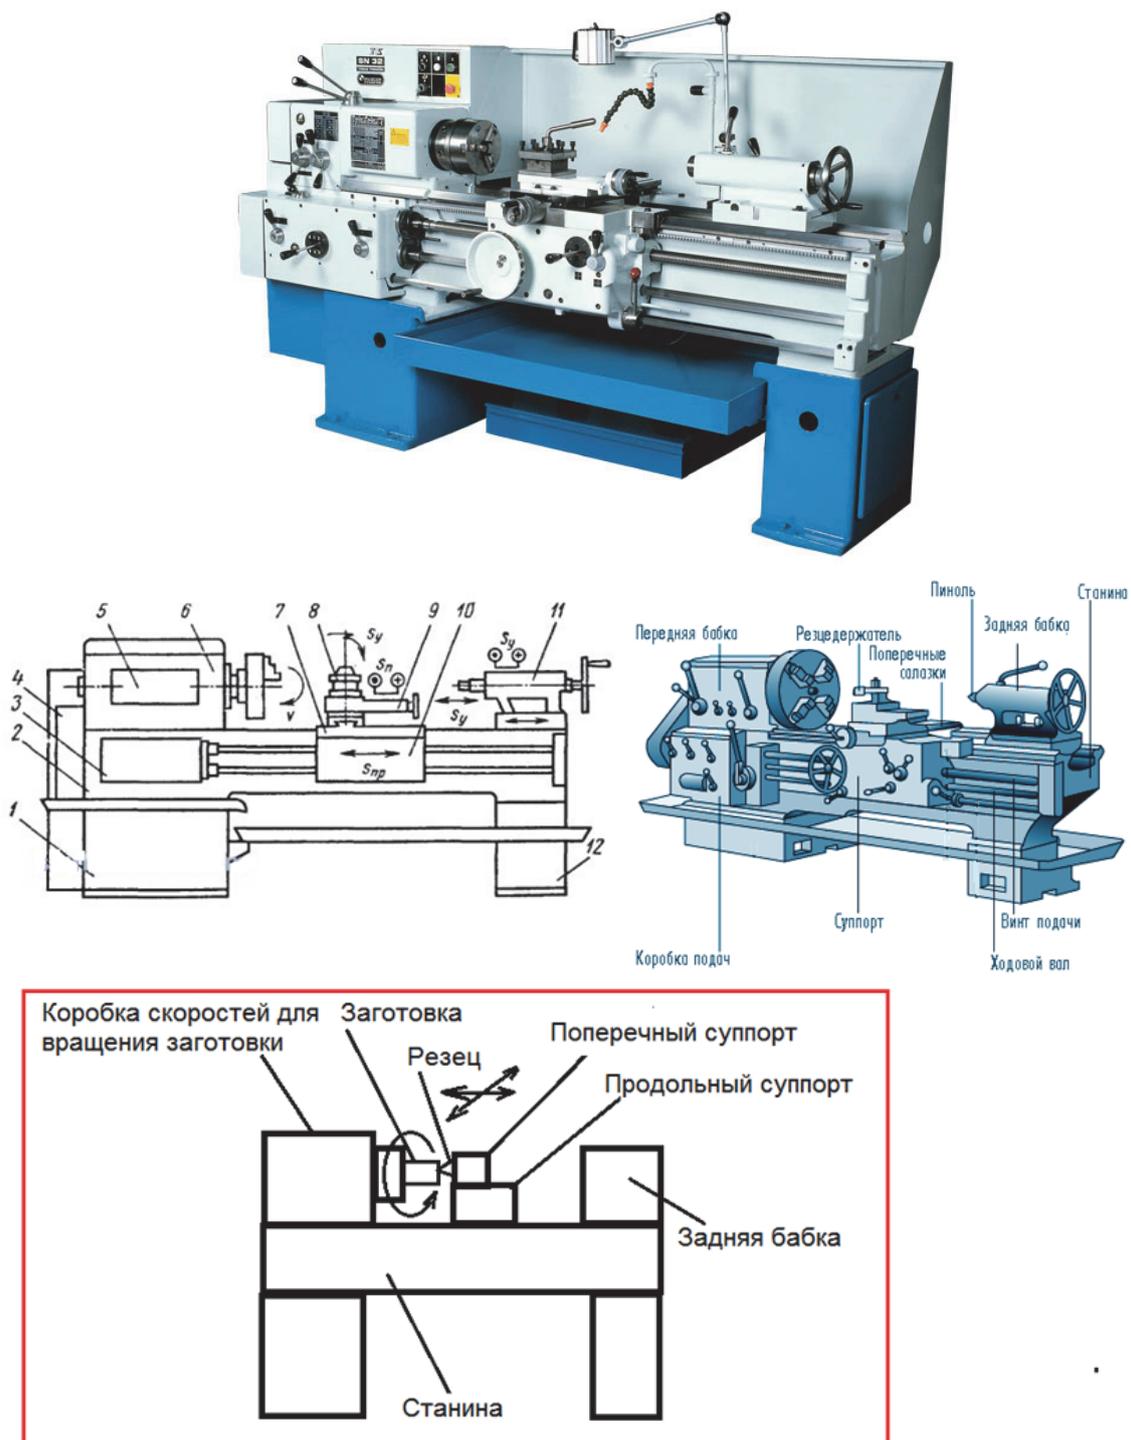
Токарно-винторезный станок и различные схемы его представления: эскиз, трехмерная модель, укрупненная схема
